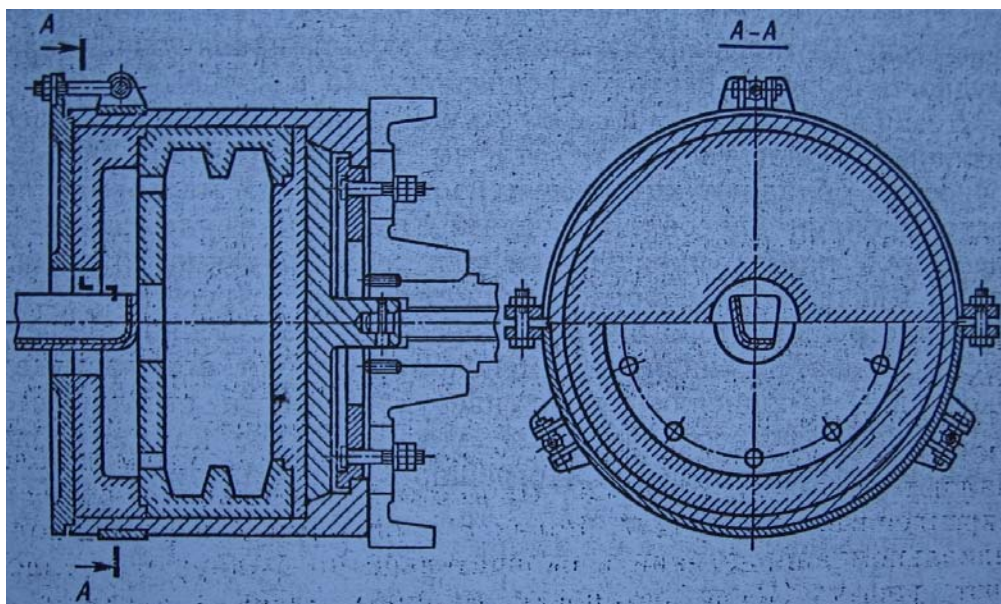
Форма для центробежной отливки, собранная из стержней.
